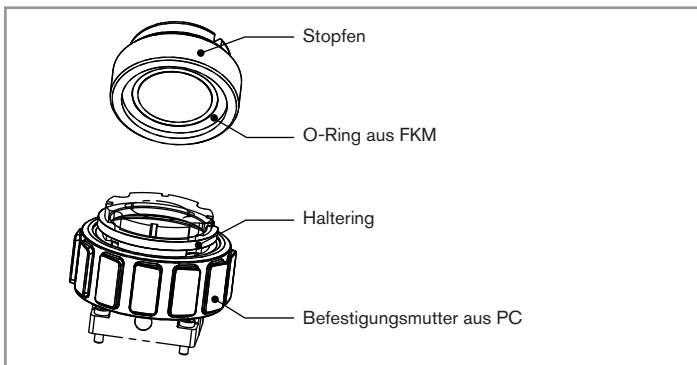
Stopfen mit O-Ring, Befestigungsmutter und Haltering
